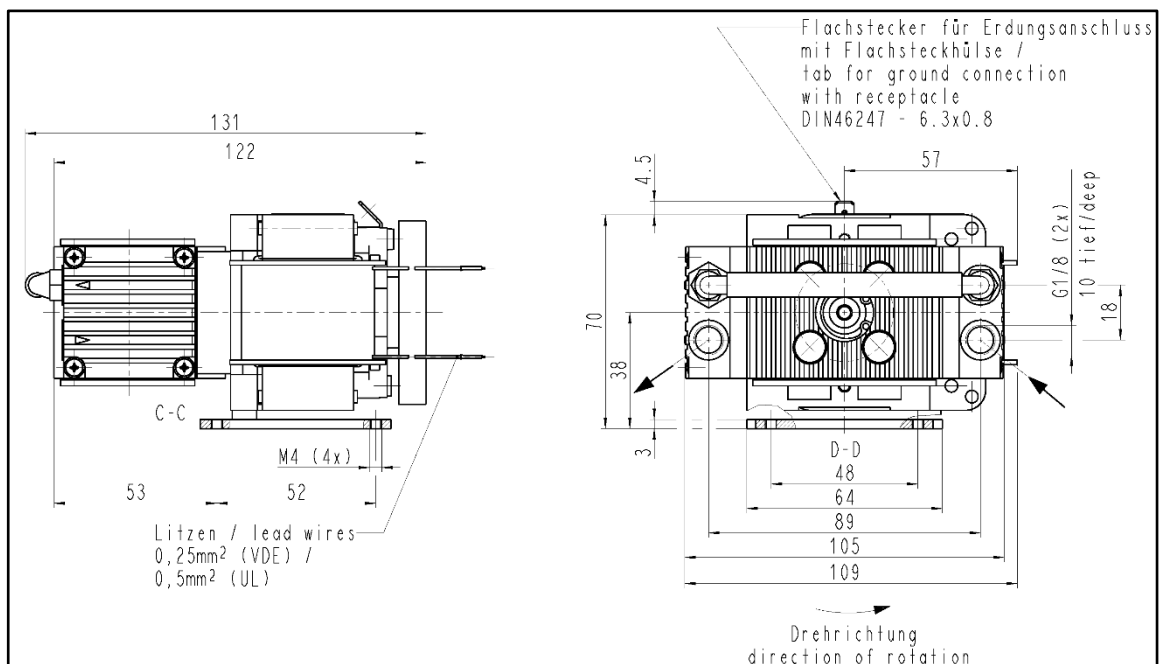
Befestigungsmaße Pumpenreihe N85.3 K_E
